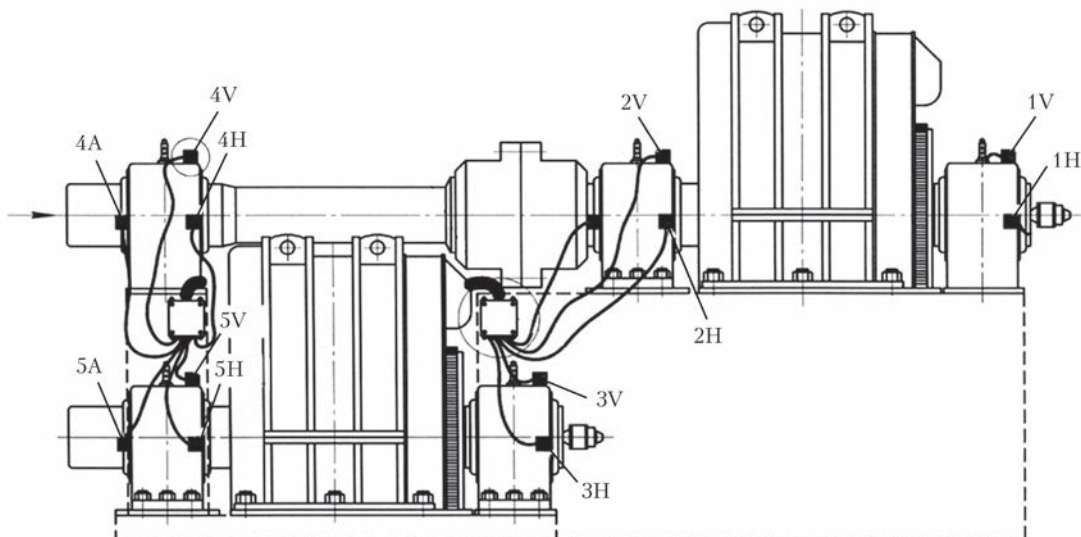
Схема расположения измерительного оборудования на ГППВ. Направления измерений: V – вертикальное; H – горизонтальное; A – осевое (цифры – номера подшипников)
